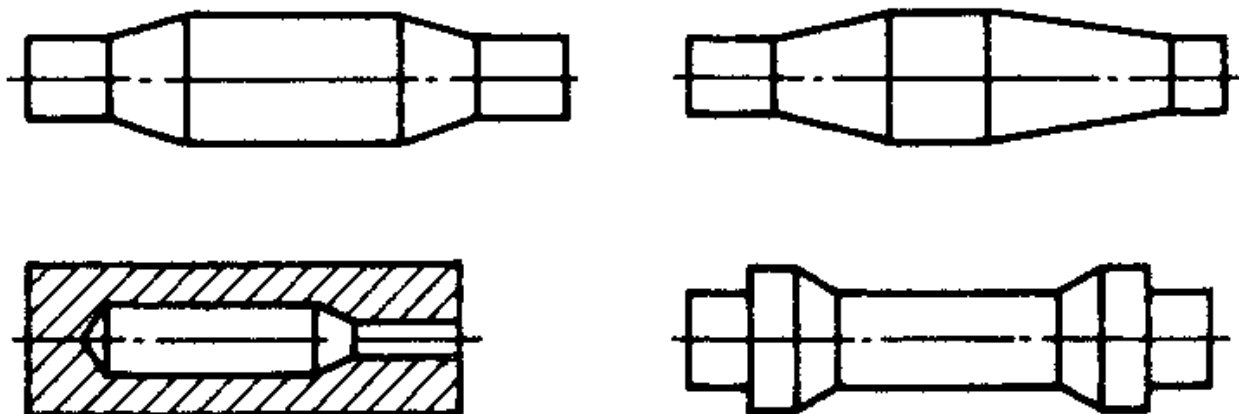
Типові заготовки, які одержують ротаційним деформуванням
